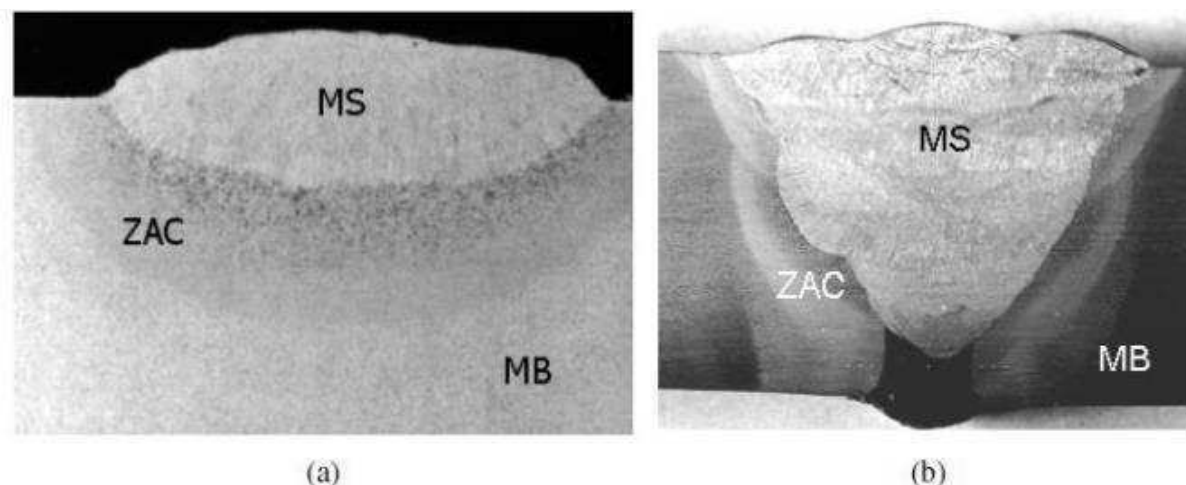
(a) solda com passe único e (b) solda com passes múltiplos (Duarte, 2014).
